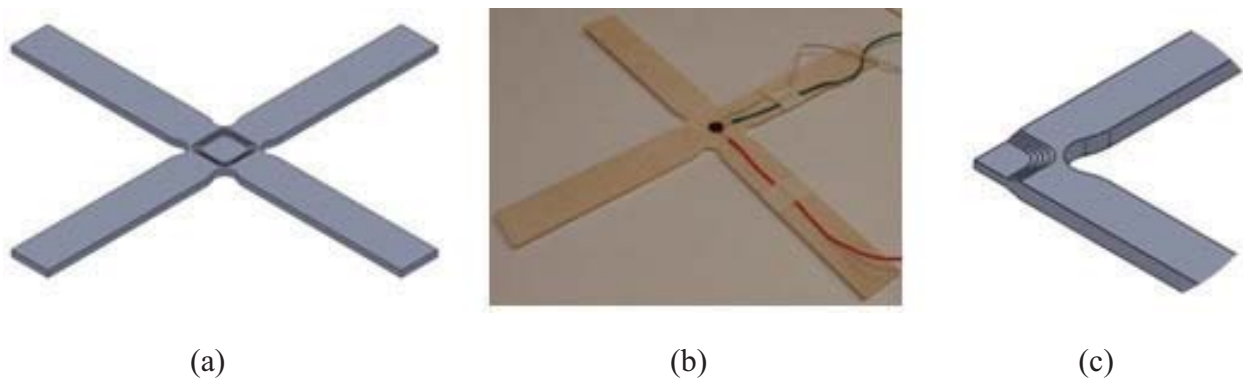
(a) Modelo 3D con SolidWorks® de la probeta cruciforme; (b) Probeta cruciforme con roseta pegada; (c) Detalle zona central rebajada.
